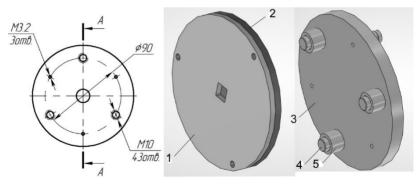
Конструктивные элементы узла трения:1 - основание; 2 - фрикционный диск; 3 - диск с образцами; 4 - Образец для испытаний; 5 - втулка
